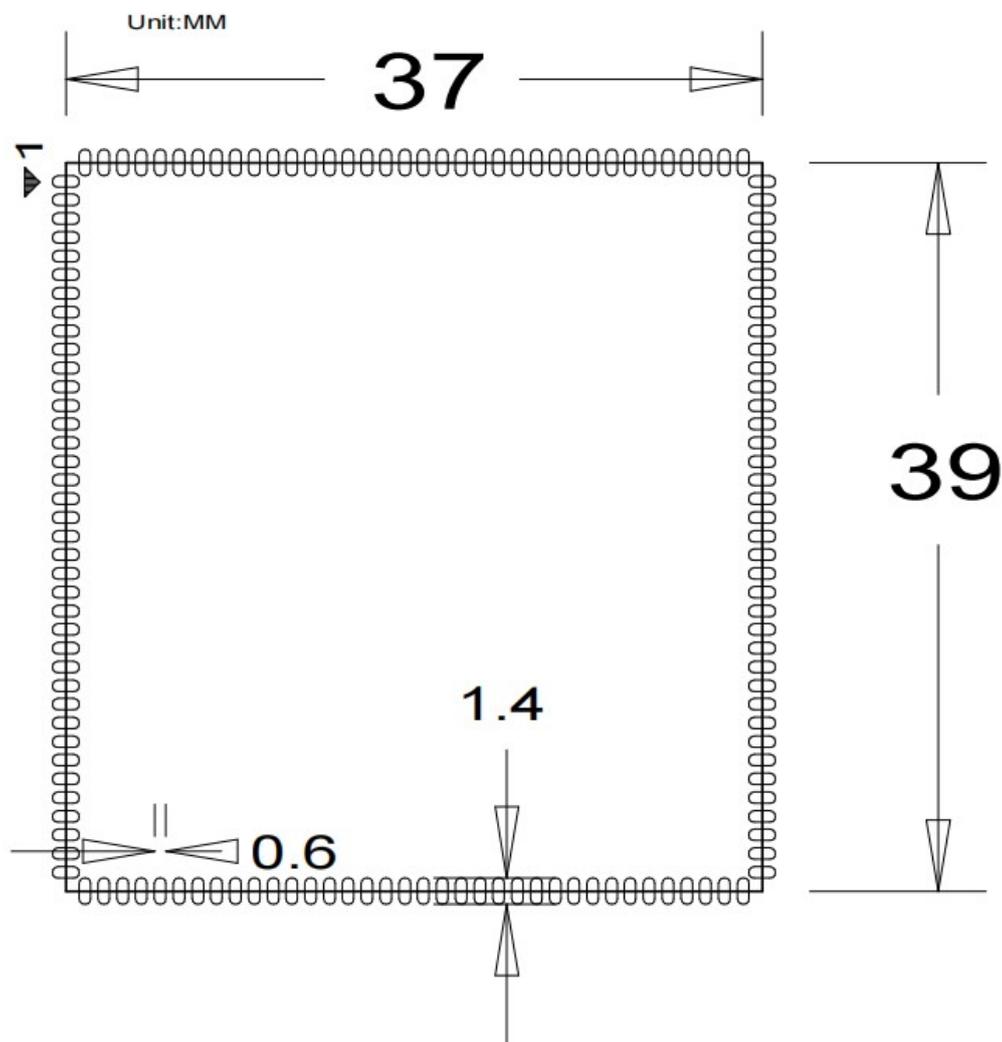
MYC-YA15XC-T 核心板 PCB 封装
